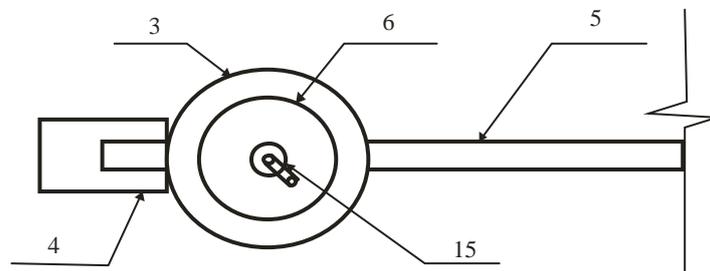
Опорно-поворотное колесо и площадка оператора (вид сверху):
